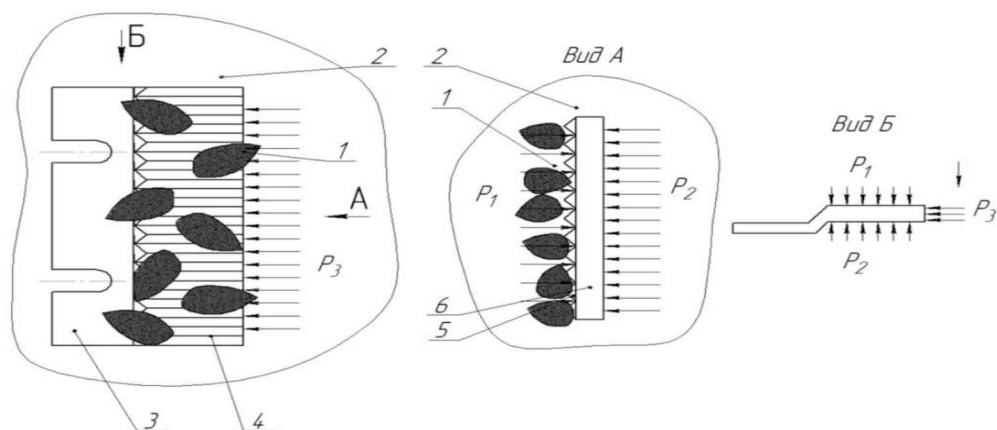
Процес взаємодії коренеплоду з ножом під час подрібнення: 1-подрібнюваний буряк; 2-нерухомий циліндр установки; 3- привалкова зовнішня площина ножа; 4 – грані ножа; 5 – ріжуча кромка ножа; 6 – порожнина сходу стружки
